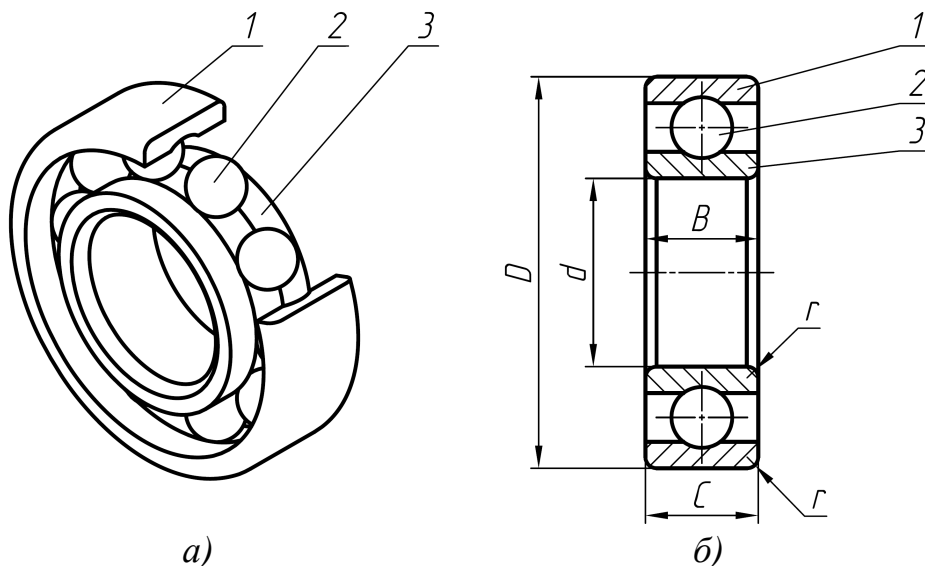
Схема підшипника а) загальний вигляд; б) основні розміри;
